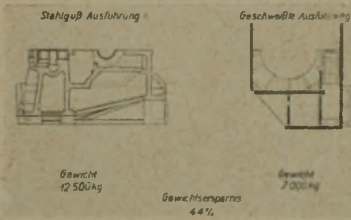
Gewichtsvergleich einer Stahlguß- und Schweißkonstruktion des Rollgangrahmens einer Blockstraße
